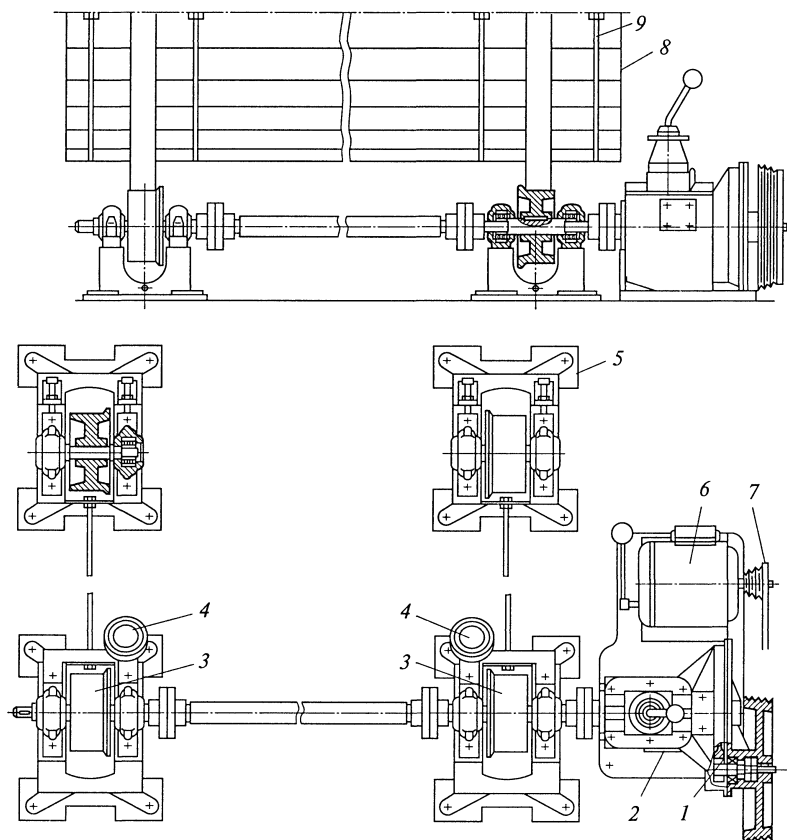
Привод барабанной сушилки фирмы «Ромет»
